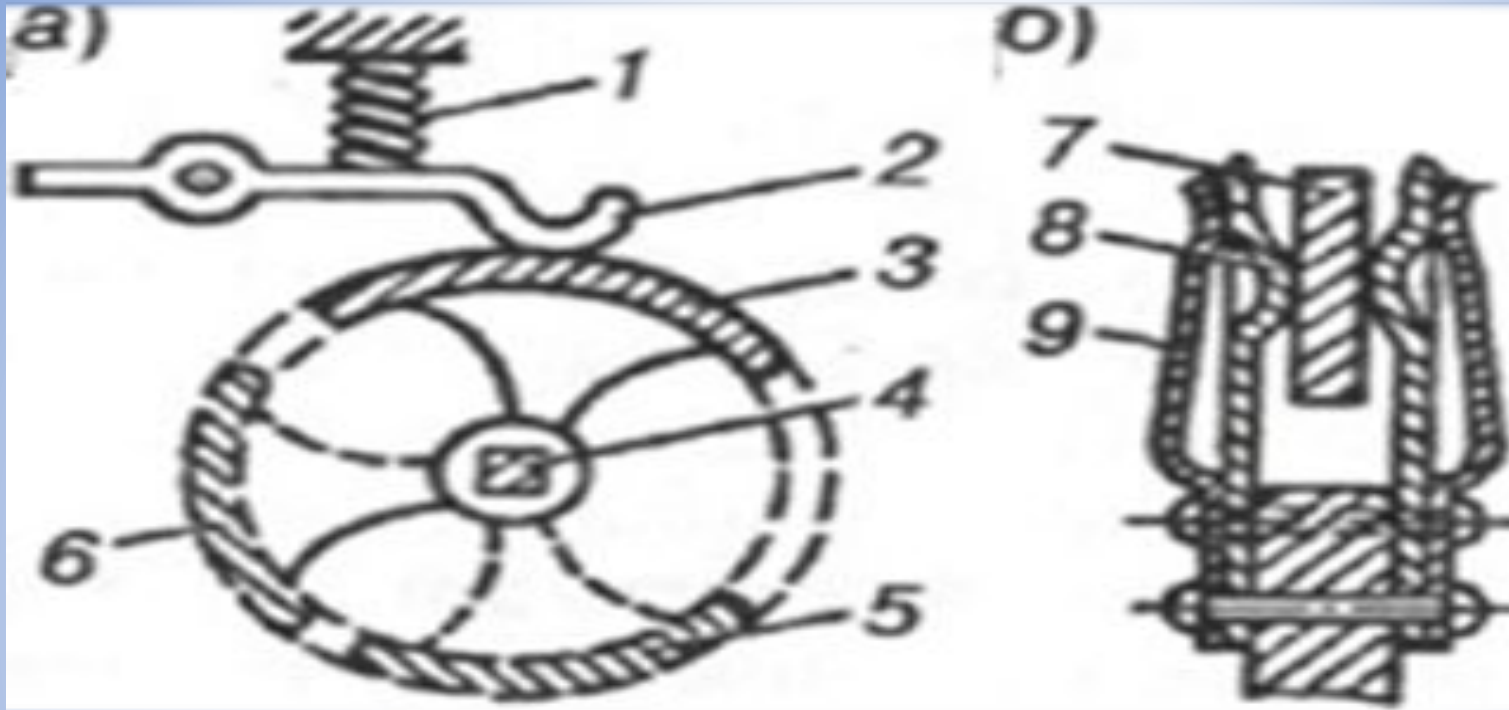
Пальцевые (а) и рубящие (б) контакты: 1 — пружина; 2 — неподвижный контакт (палец); 3, 5, 6 — подвижные контакты; 4 — ось; 7 — латунный нож; 8 — неподвижный контакт; 9 — пружина
